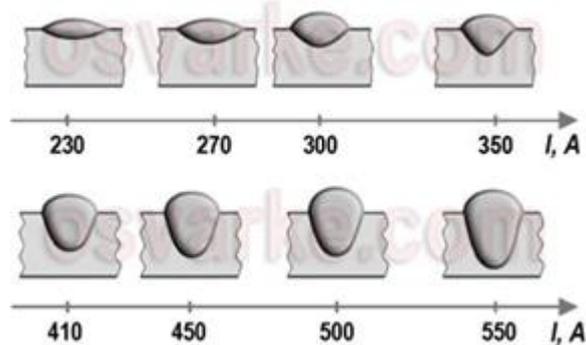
Влияние тока на форму и размеры сварного шва
